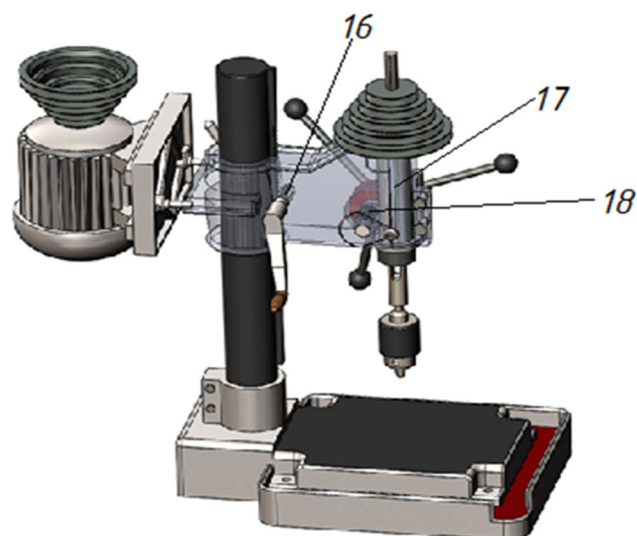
Конструкція внутрішнього механізму свердлильного верстата НС- 12А
